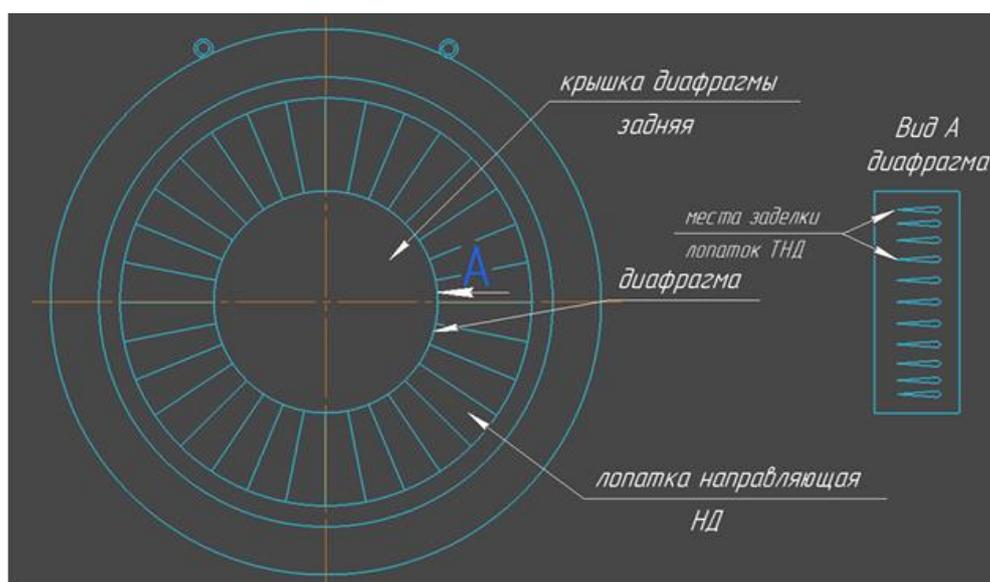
Вид обоймы 186.003СБ со стороны задней крышки (вид на направляющие лопатки турбины низкого давления)
